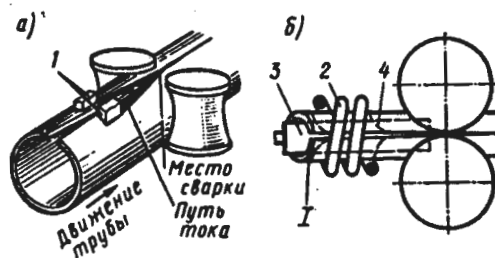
Схема контактной сварки труб токами высокой частоты:
